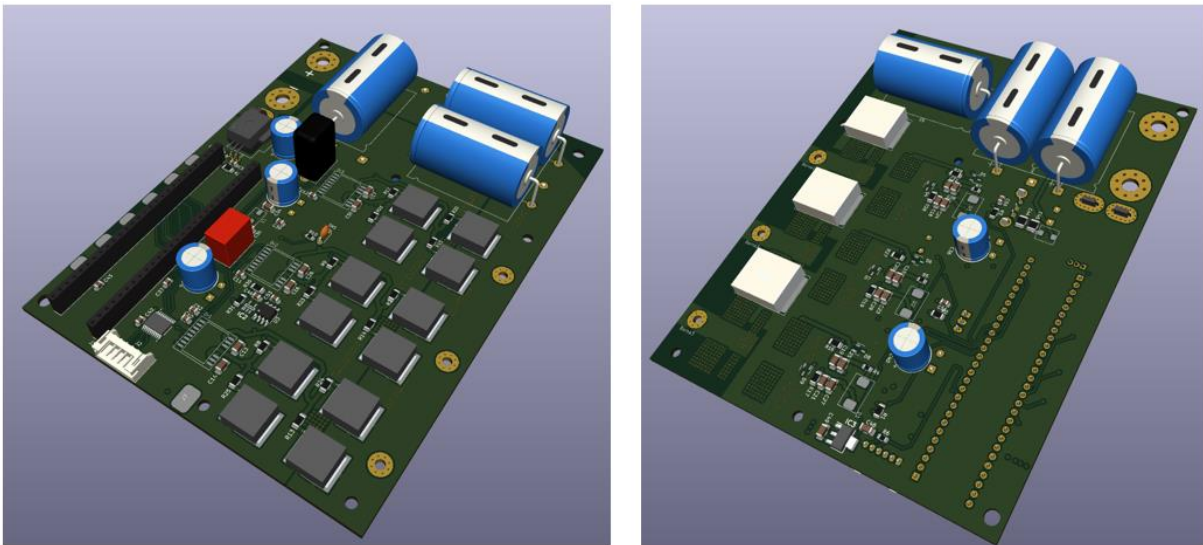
PCB en 3D per la part superior a l'esquerra i la part inferior a la dreta.
